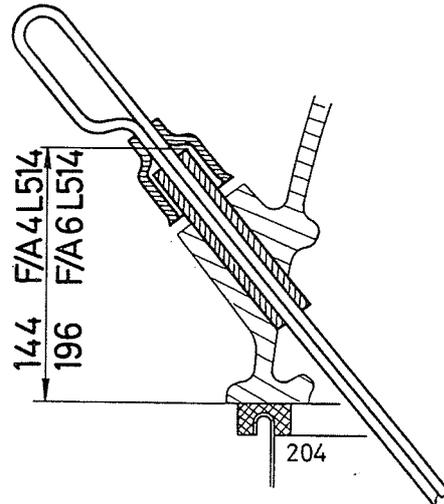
Einbau des Führungsrohres zum Ölpeilstab F/A 4-6L 514
